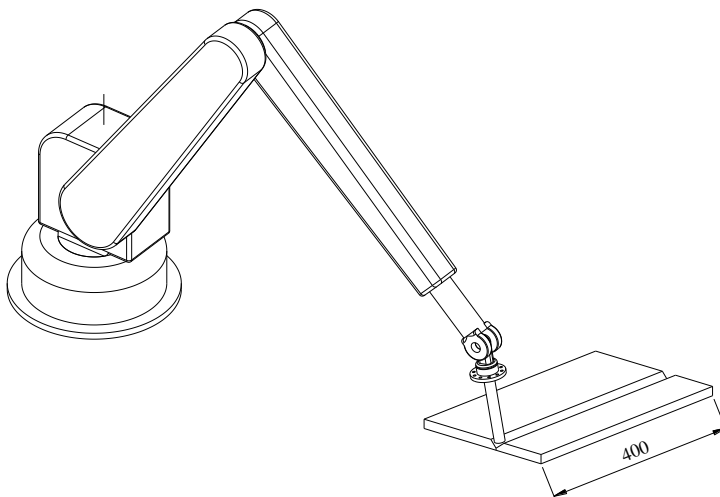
Soudage de deux tôles (bout à bout) par un robot à 6 axes
